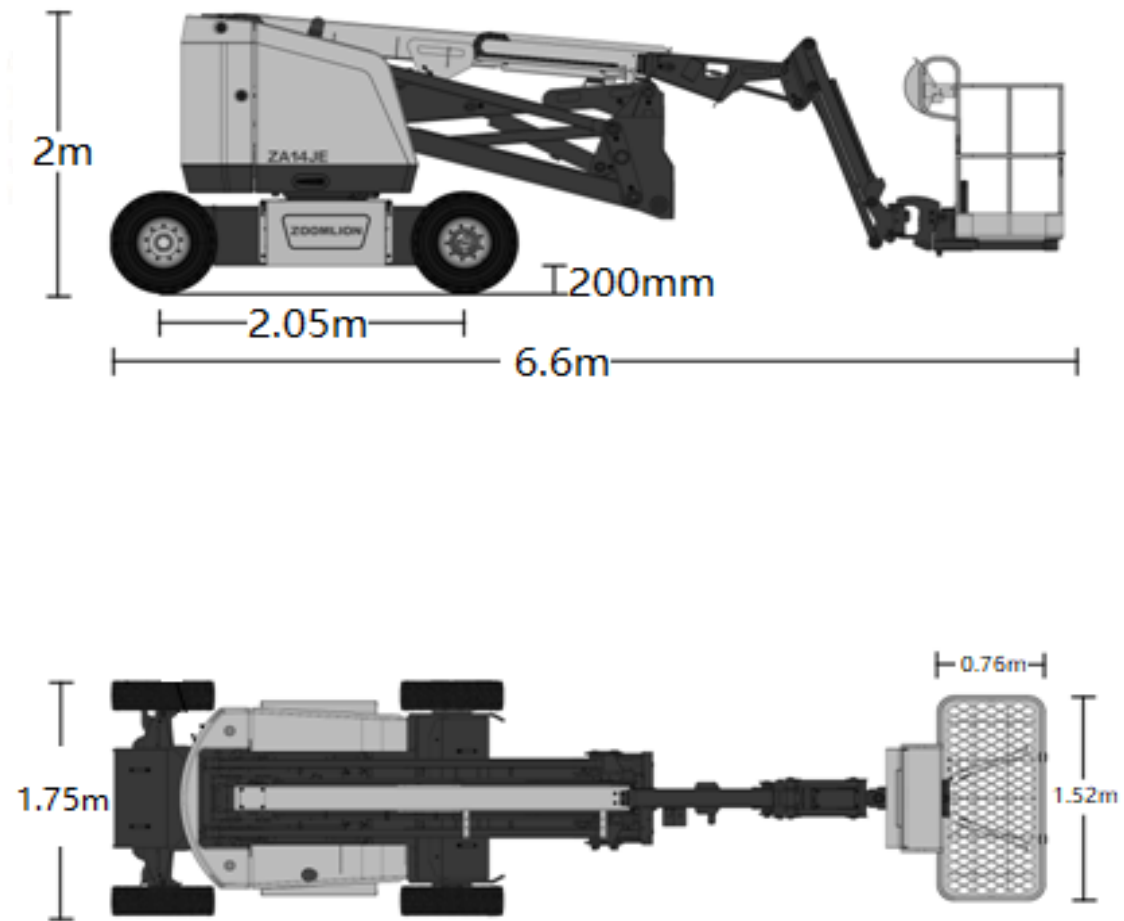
Dimensiones en condiciones de conducción de la plataforma elevadora ZA14JE-Li
